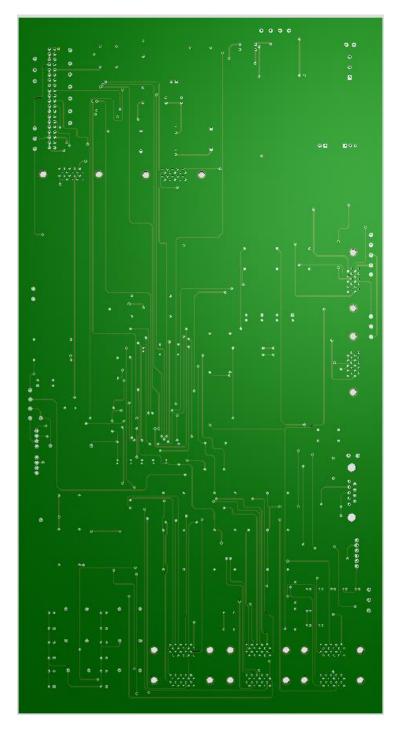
PCB layout 4 lớp của mạch tổng hợp CNC 5 trục.
